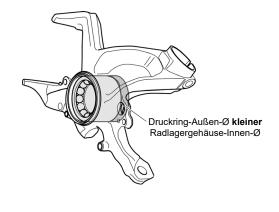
Ermitteln der Abmessungen: Radlager Ausbau
